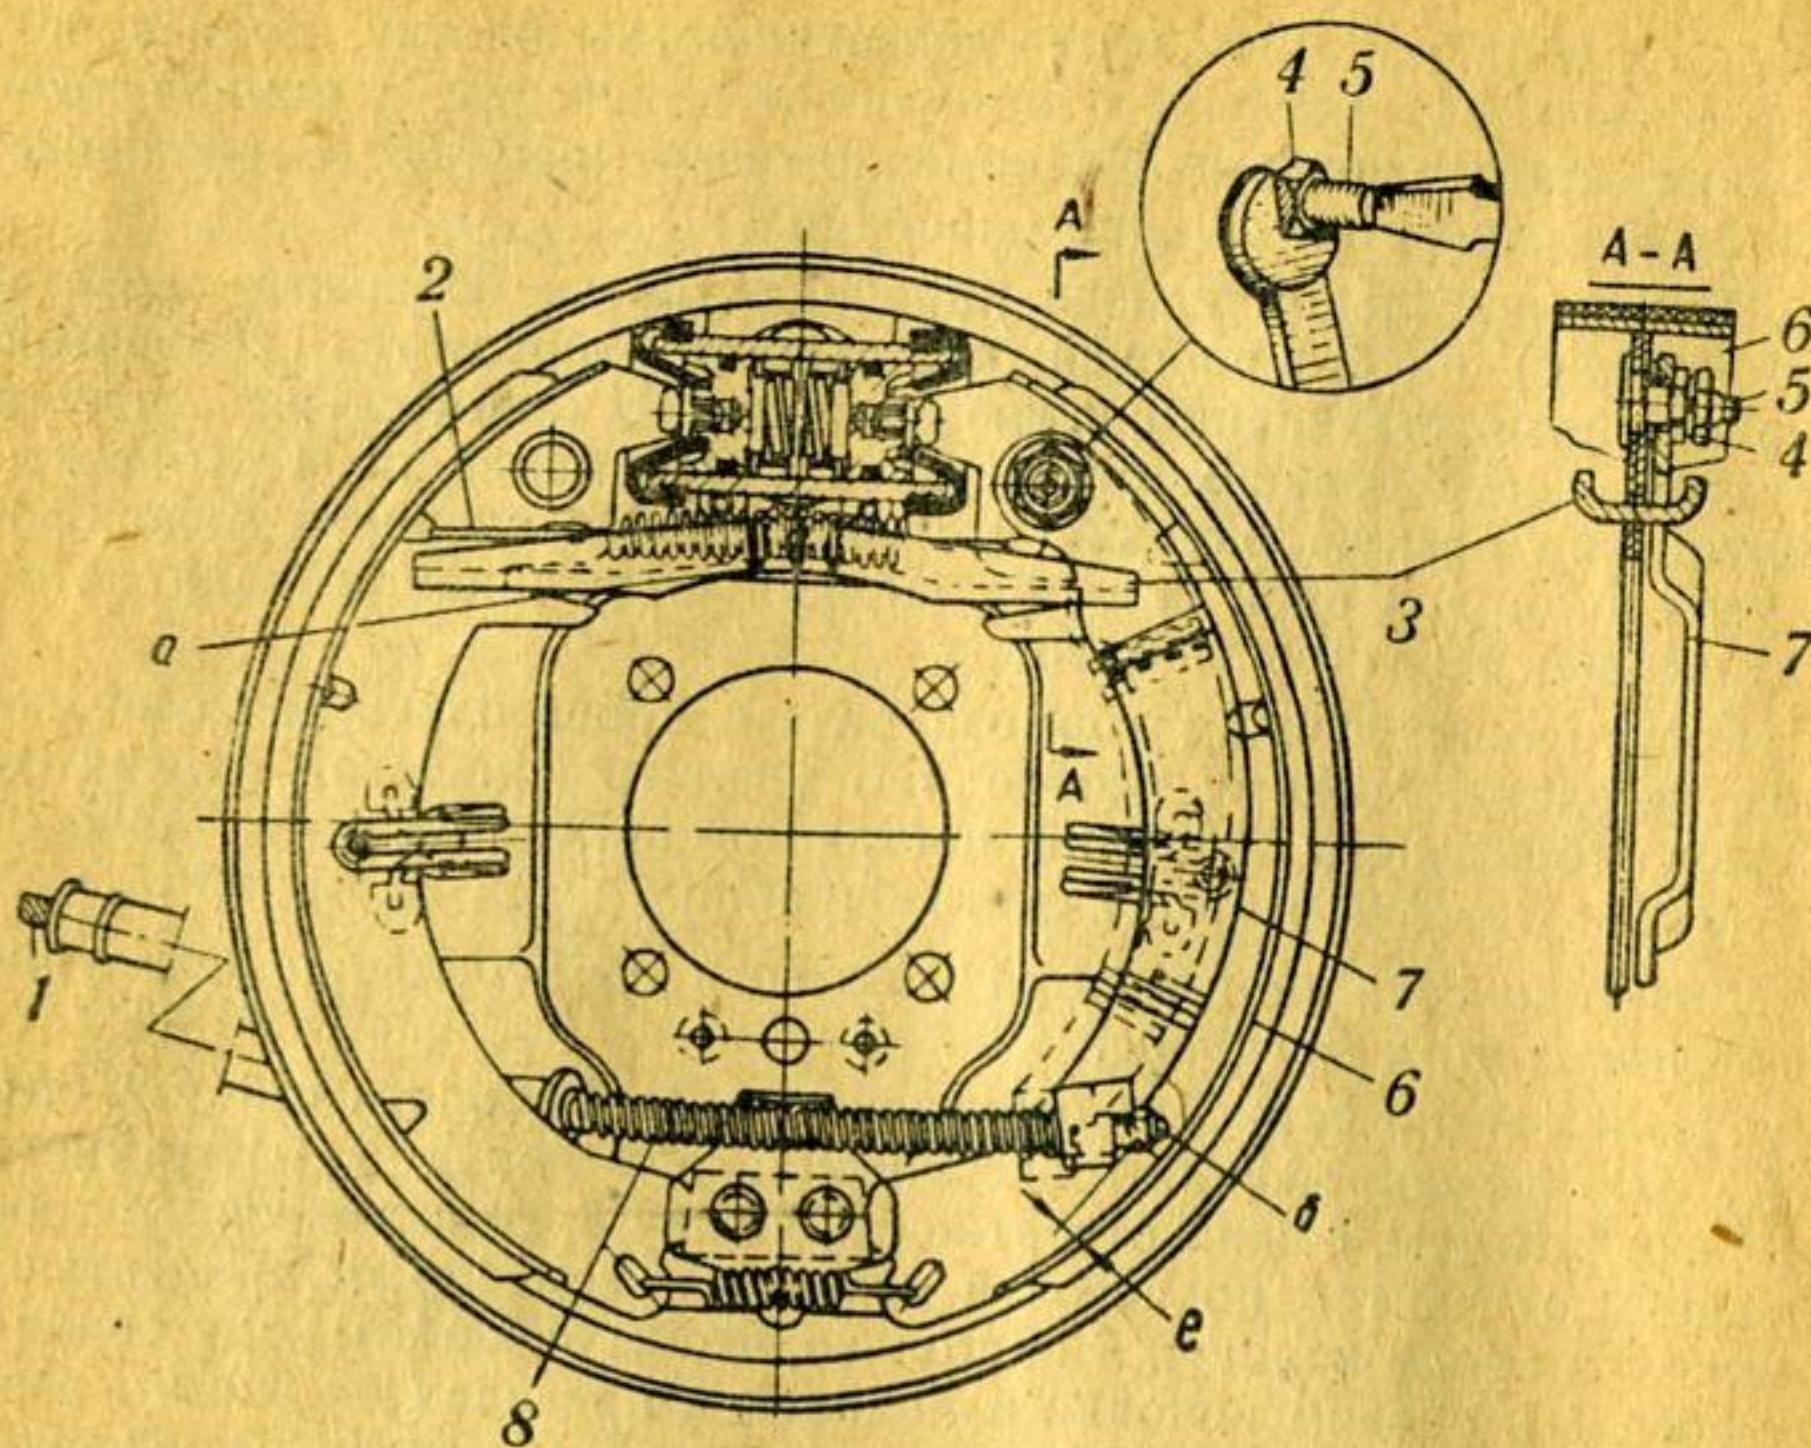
Регулировка положения разжимного рычага на задней колодке тормоза:
